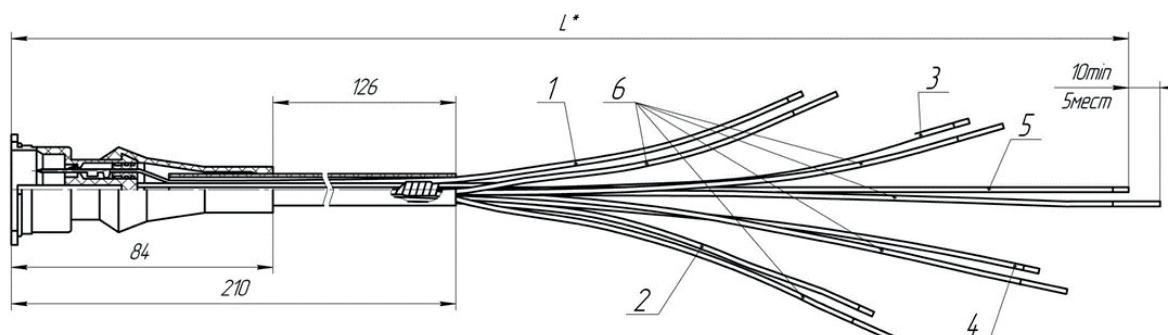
Вилка с армированными проводами СЦАЗ-2-6-Р
